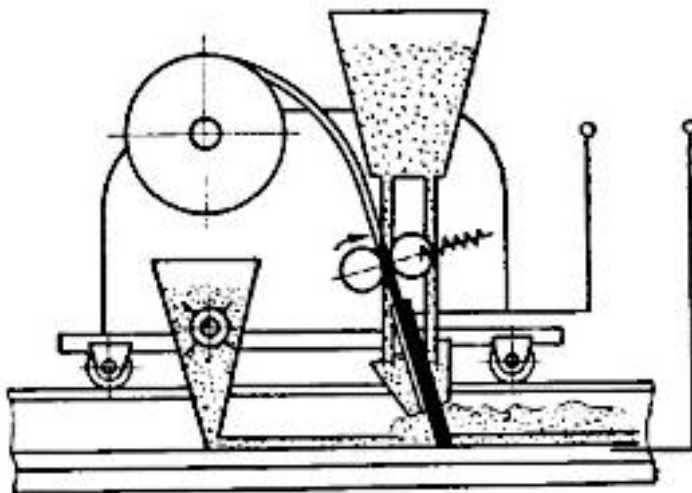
Общий вид установки для автоматической наплавки под слоем флюса ленточными электродами
